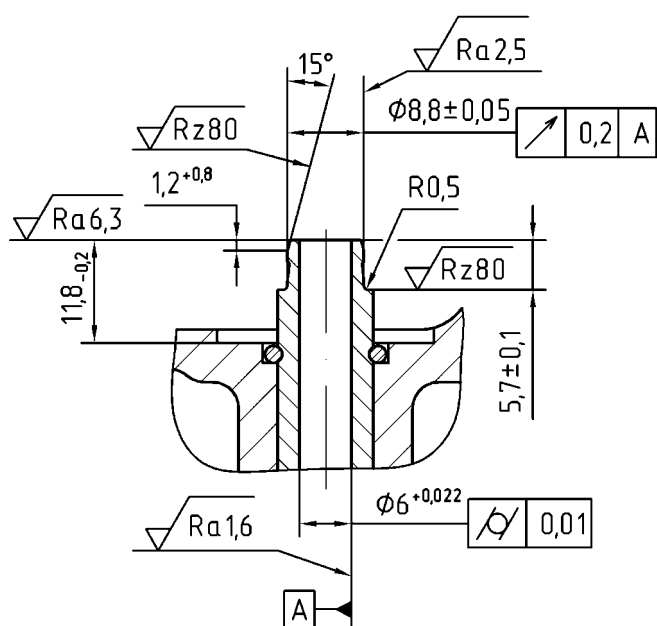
Обработка направляющих втулок клапанов после запрессовки их в головку цилиндров
